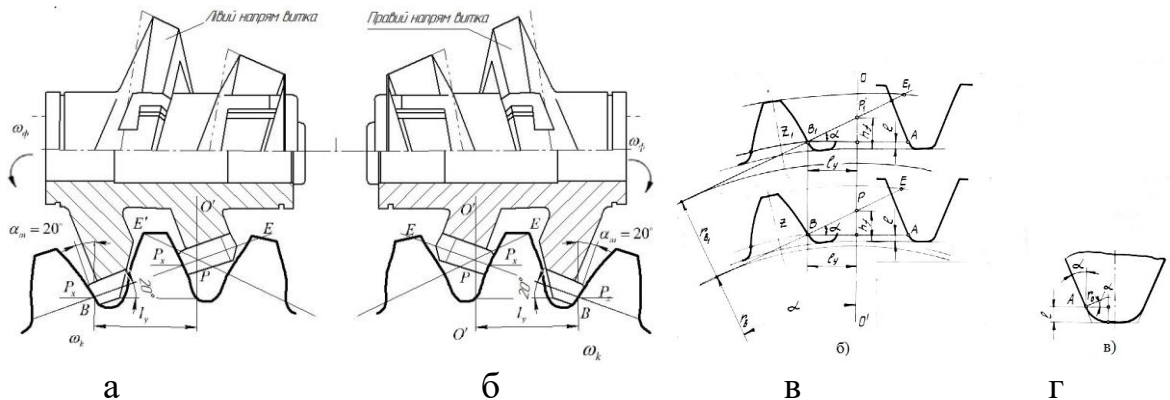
Новий спосіб обробки зубів черв'ячною фрезою з роздільною схемою формоутворення: а - схема установлювання фрези; б - зв'язок установлювальної відстані з кількістю зубів колеса; в - параметри вершини зуба чорнової фрези
